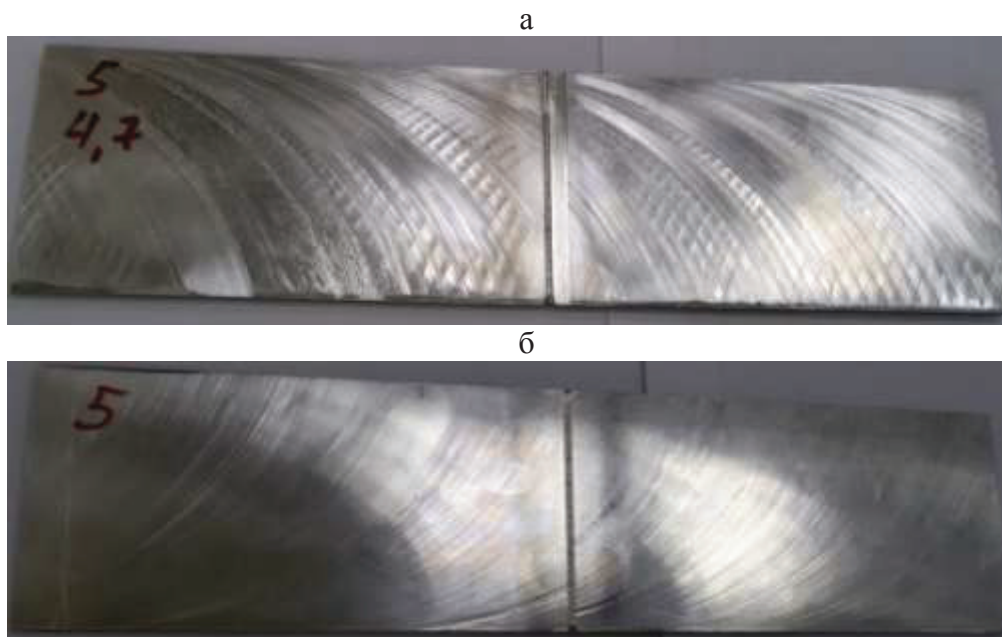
Внешний вид образца № 5 из алюминиевого сплава марки АК4-1Ч Т1 после процесса лазерной сварки с 2-х сторон:
